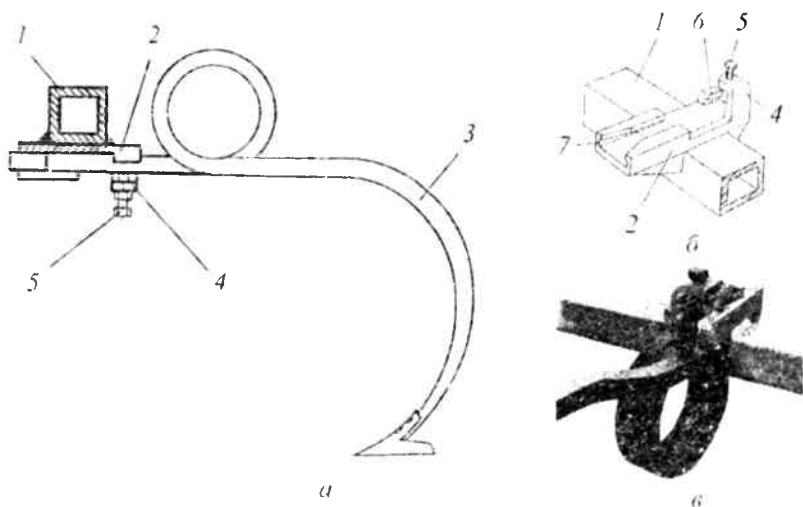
Новый узел крепления пассивного рабочего органа на упругой стойке: *а - общий вид; б - в аксонометрии; в - в натуре: 1 - рама; 2 - корпус; 3 - стойка; 4 - зажим; 5 - стопорный болт; 6 - упор; 7 - торцевая уширенная часть узла крепления
